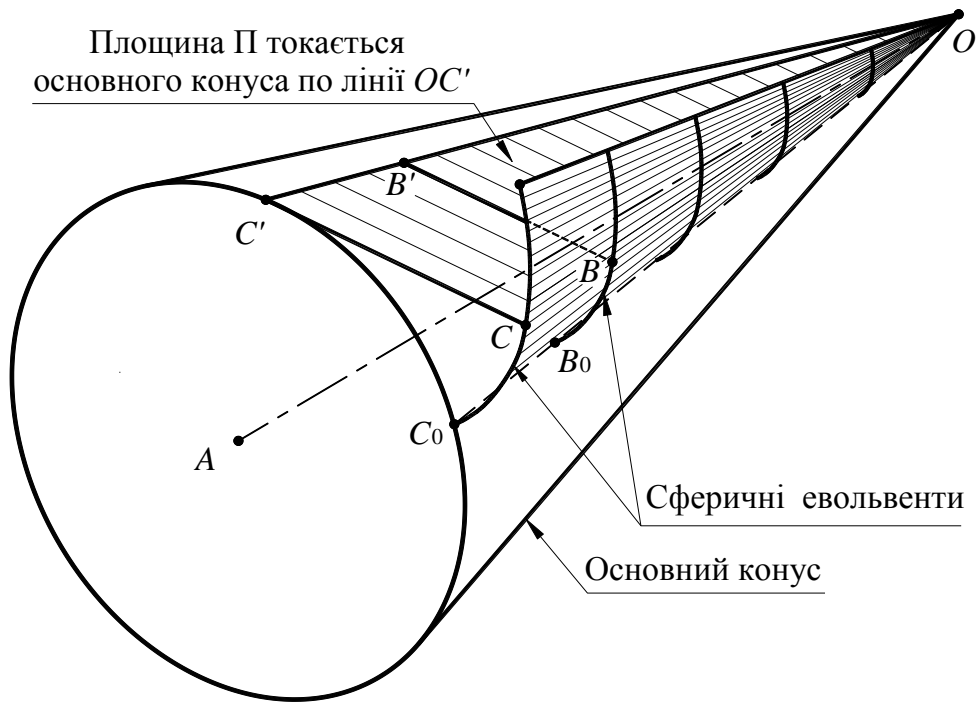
Утворення бокової поверхні зубця конічного колеса
